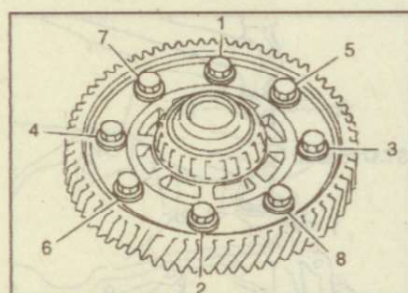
Последовательность затягивания болтов крепления ведомой шестерни главной передачи
